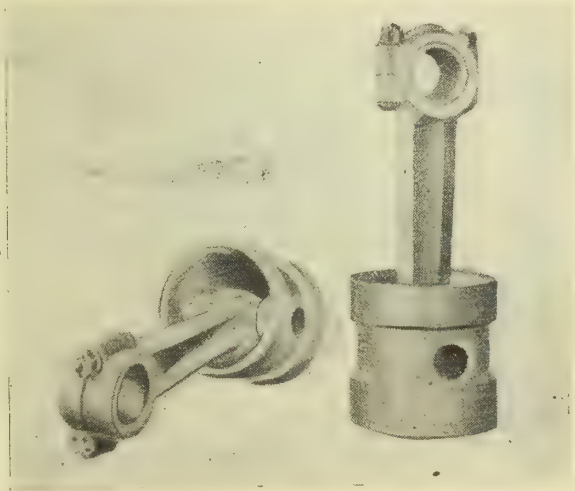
Assemblage de pistons et bielles d'aluminium.
